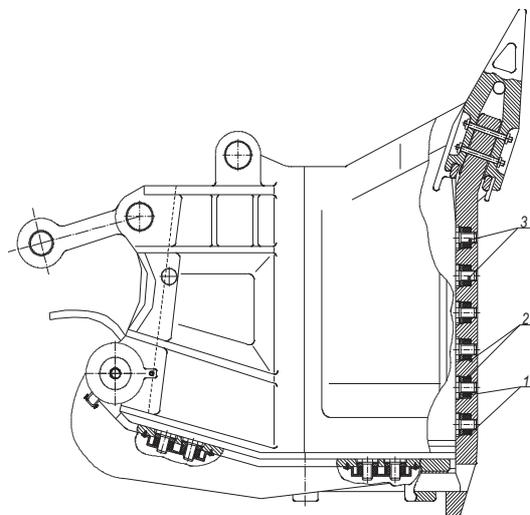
Ковш экскаватора с прямой лопатой, оборудованный пакетными пьезокерамическими трансдюсерами
